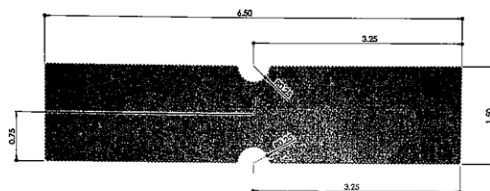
Dimensiones de la placa con las muescas, las dimensiones están en plg.
